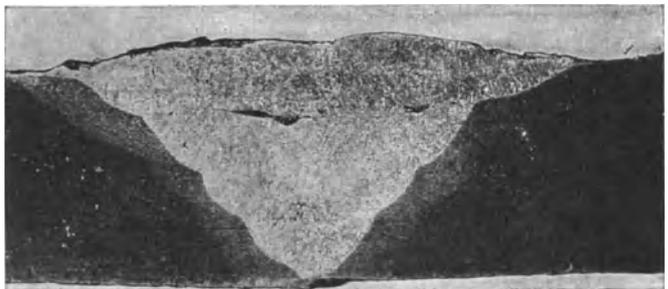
Querschnitt einer Lichtbogenschweißung.
